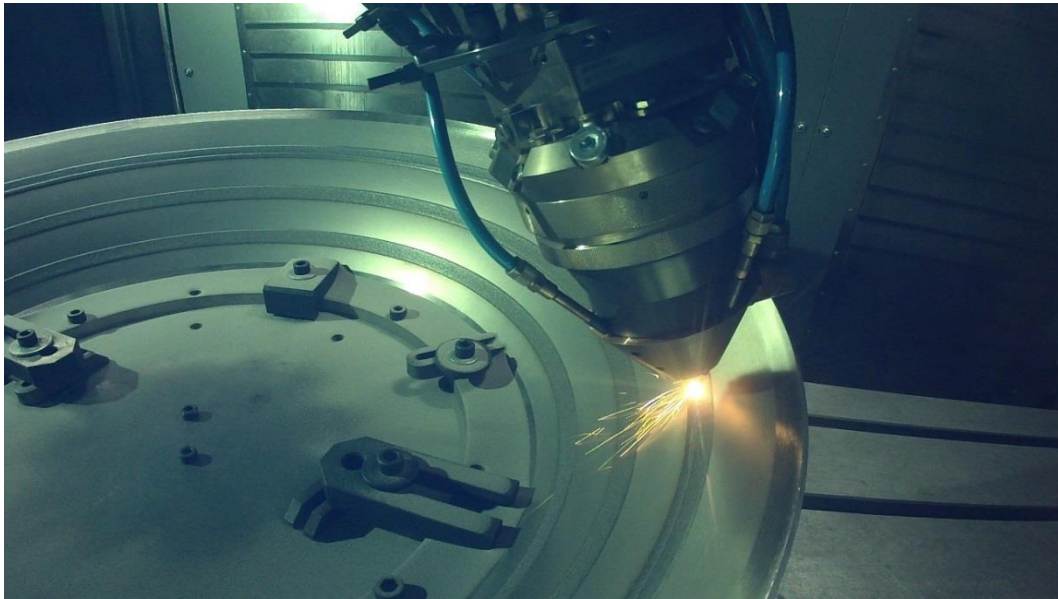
Proceso de aporte en condiciones de baja potencia para reparación y fabricación de detalles por aditivo en carcasas de turbinas de baja presión.
